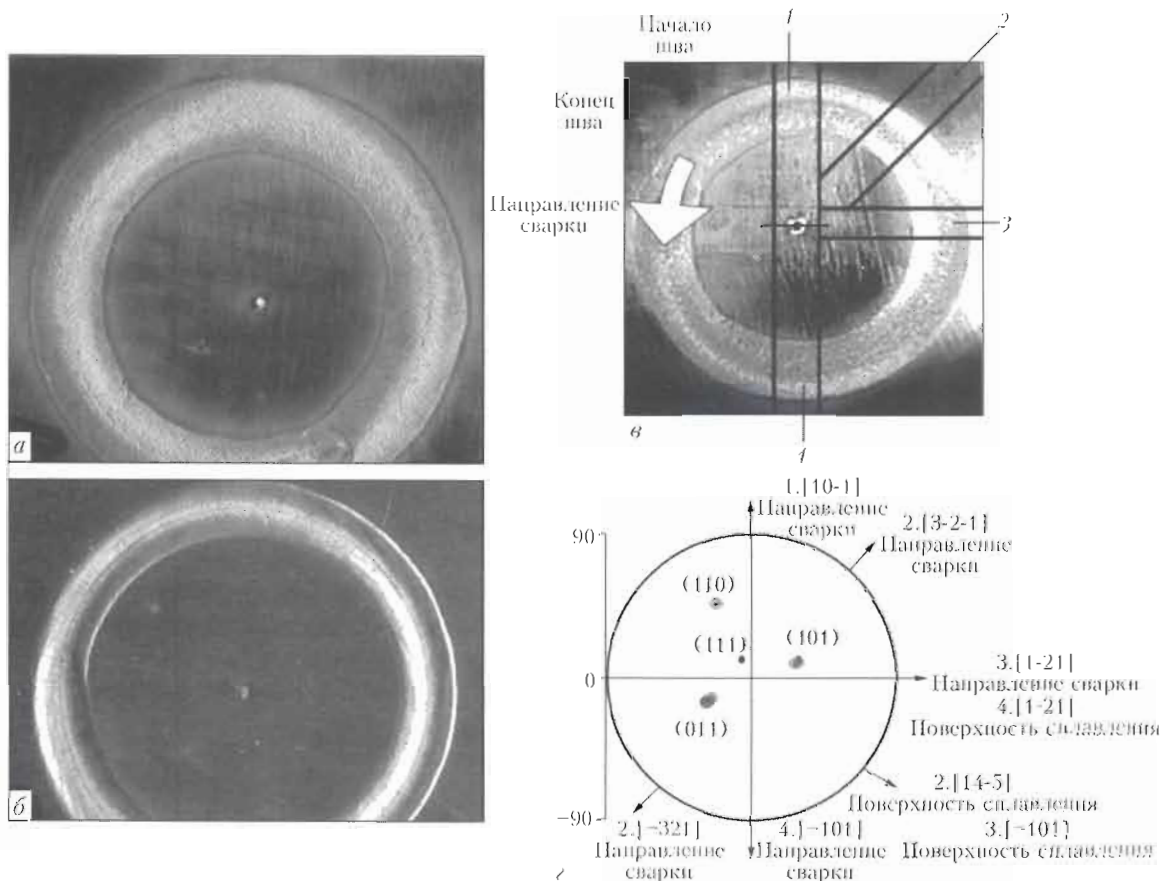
Внешний вид кольцевых швов при скорости сварки 10 (а) и 60 м/ч (б); схема вырезки образцов для исследований (в); стереографическая ориентация кольцевой пробы (z): 1-4 — номера образцов
